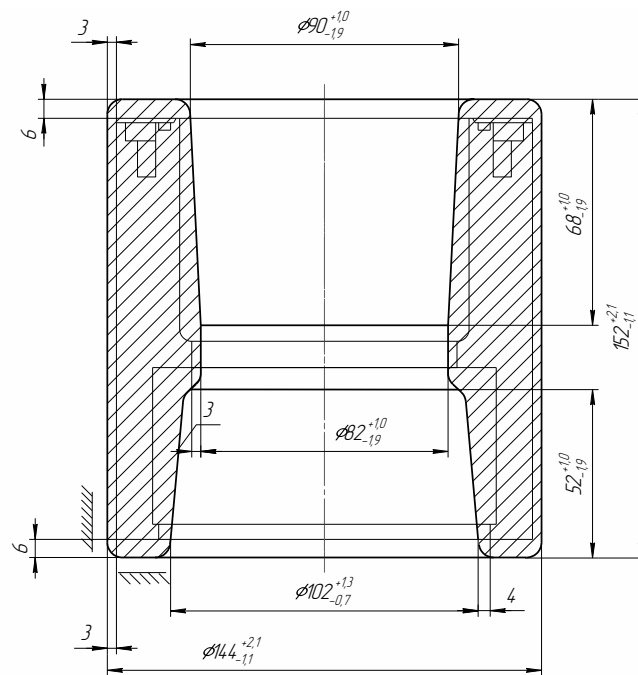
Ескіз заготовки «Корпусу ЦФ7.180.187»
